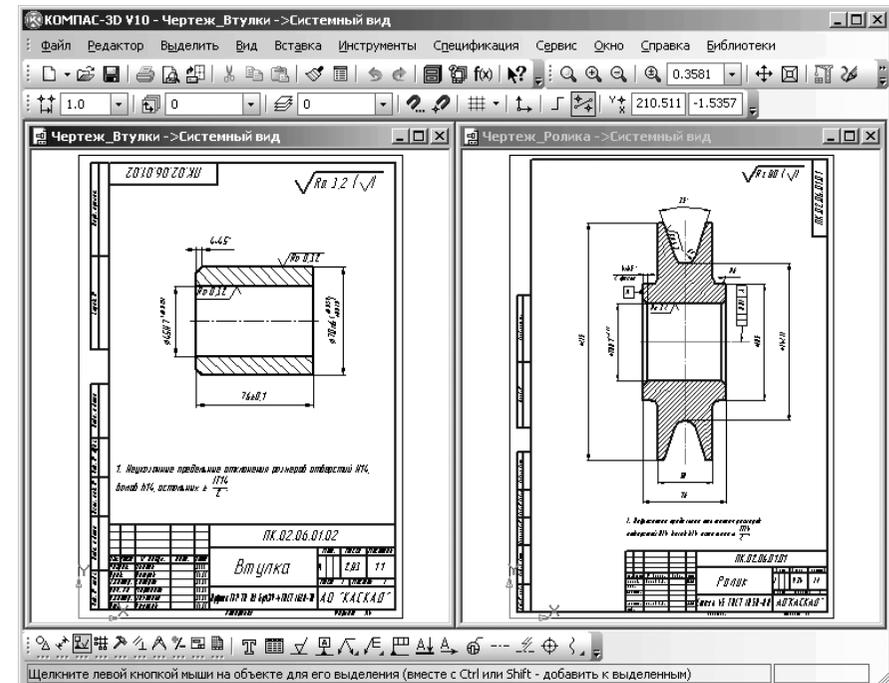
Представление деталей перед созданием сборочного чертежа Ролик\_Втулка
